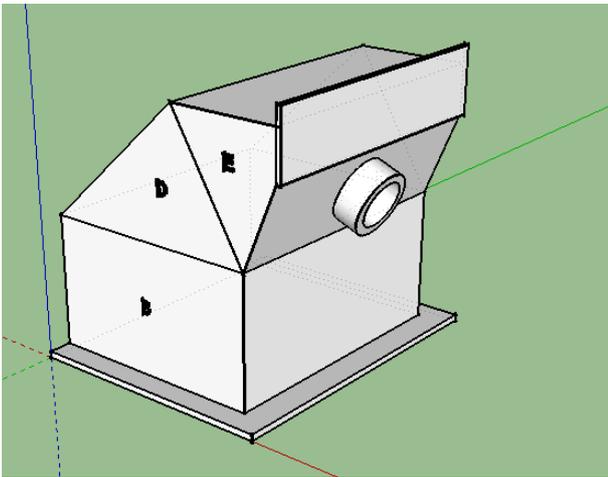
Модель алюминиевой сварной конструкции
